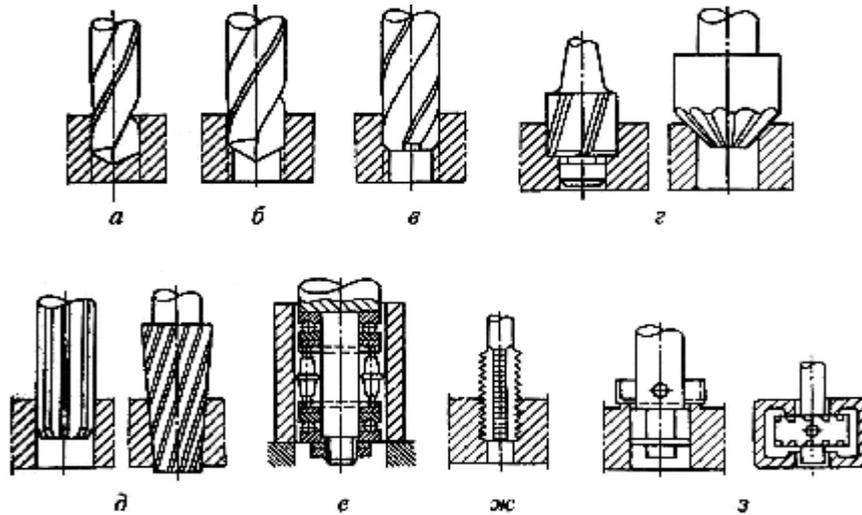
Виды обработки отверстий в заготовках: *а* – сверление; *б* – рассверливание; *в* – зенкерование; *г* – зенкование; *д* – развертывание; *е* – раскатывание; *ж* – нарезание внутренней резьбы; *з* – подрезание (цекование) торцов
